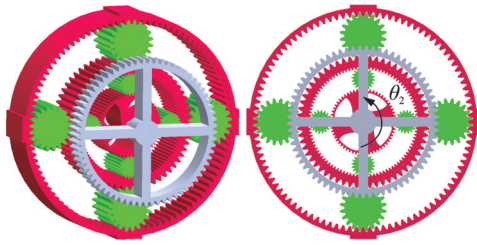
由行星齿轮组和异形轮辐齿轮构成的超材料
